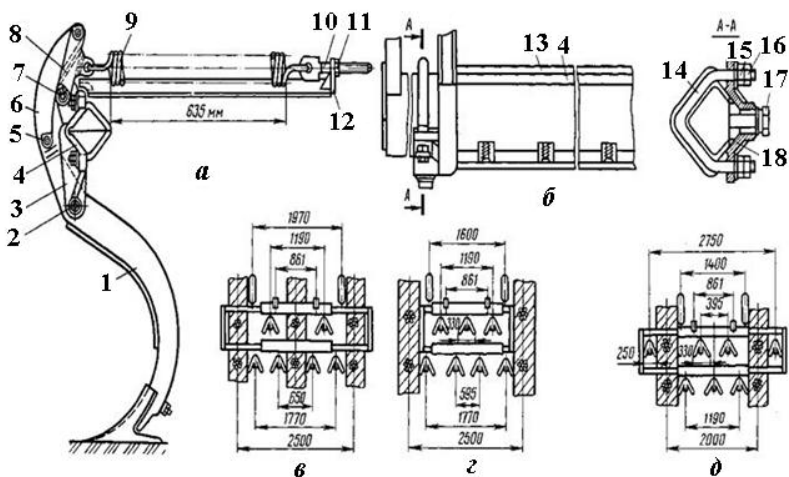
Схема робочого органу (лапа) культиватора-розпушувача КРТ-3 [9]:
